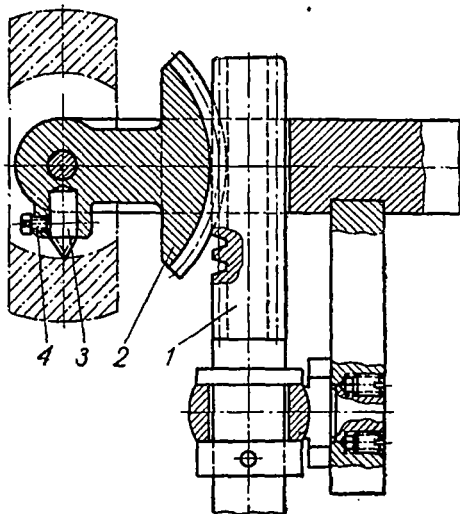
Приспособление с червячной передачей для расточки внутренних сферических поверхностей.
